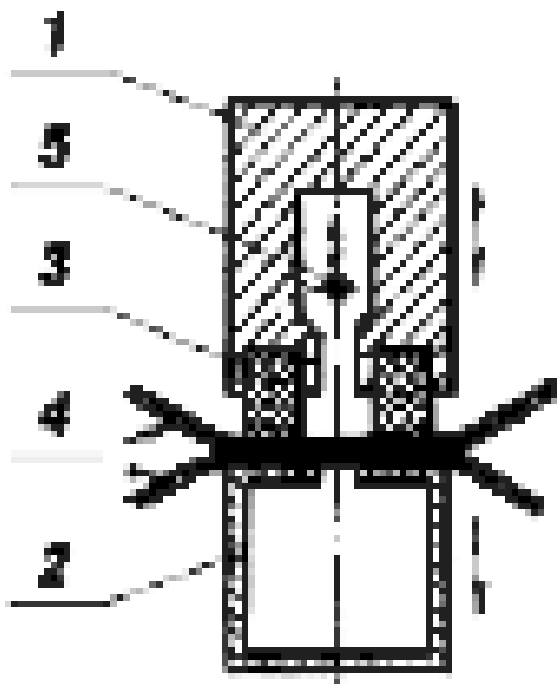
Пристрій для зварювання та різання плівки поліетиленової дротом.
